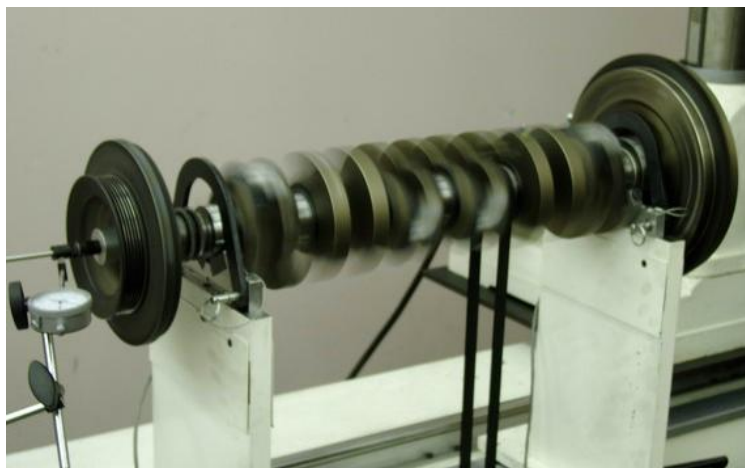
Балансировка коленчатого вала в сборе с передним шкивом, маховиком и сцеплением
